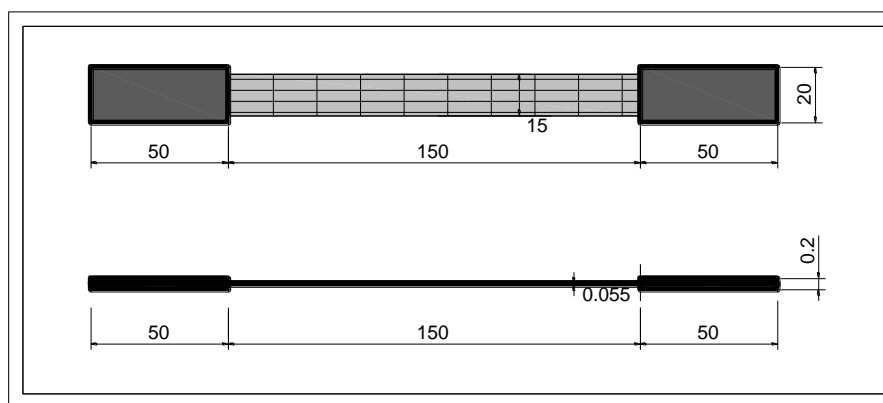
Dimensões dos corpos-de-prova segundo a norma ASTM D3039/3039M.
